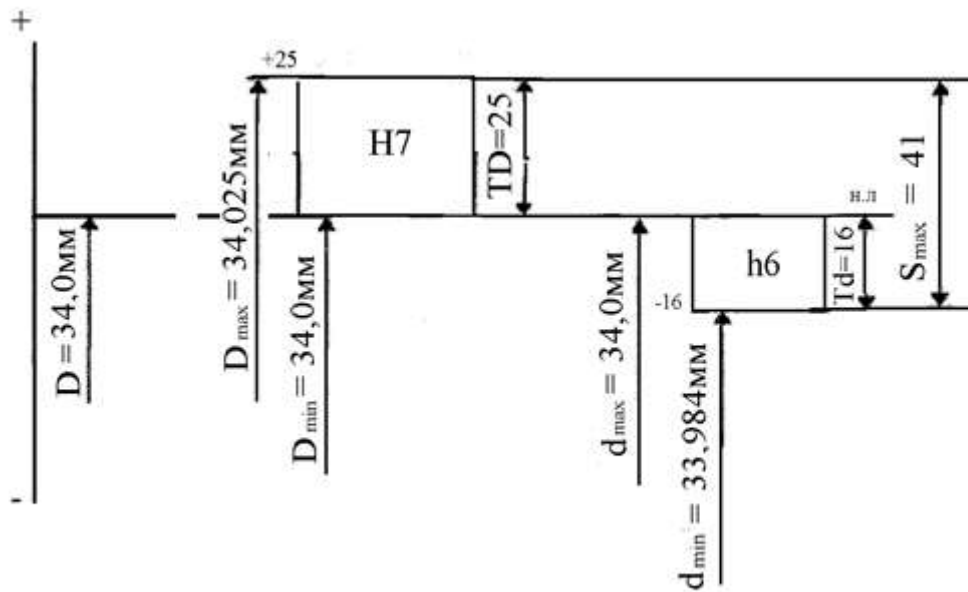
Схема расположения полей допусков посадки с зазором
